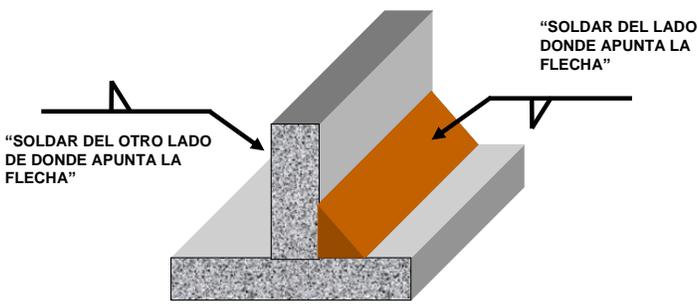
Elementos De Un Símbolo De Soldadura
